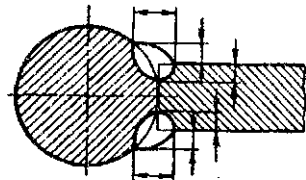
Поперечное сечение нестандартного сварного шва
